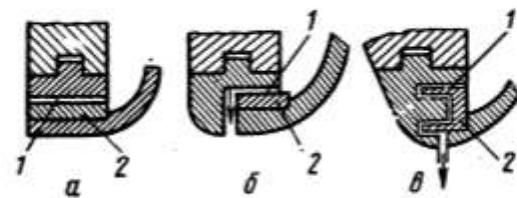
Конструкции щелевых уплотнений между рабочим колесом и корпусом насоса: а — кольцевого; б — углового; в — лабиринтного; 1 — зазор; 2 — уплотняющее кольцо
